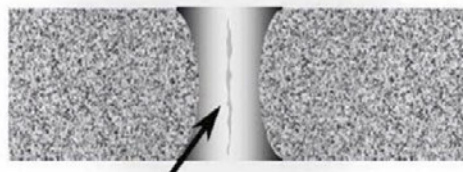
Metal fundido no expulsado del área de soldadura durante la compresión de cordón de soldadura en HFW.
